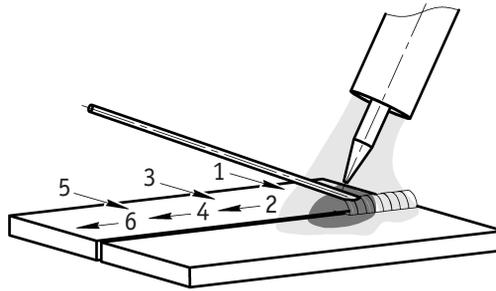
Пример манипуляции присадочной проволокой при TIG сварке.
